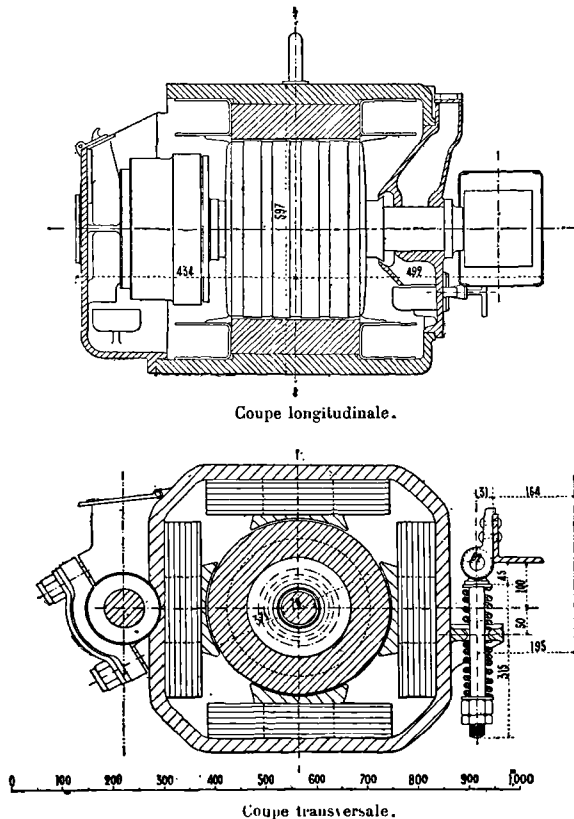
Moteur Sprague de Fives-Lille. — Coupes.
